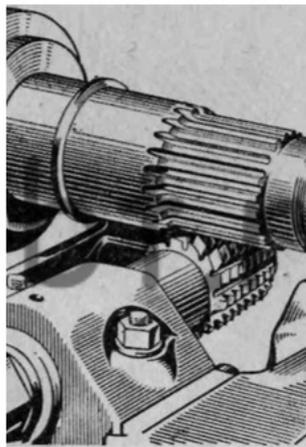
Схема нарезки шлицов червячной фрезой
